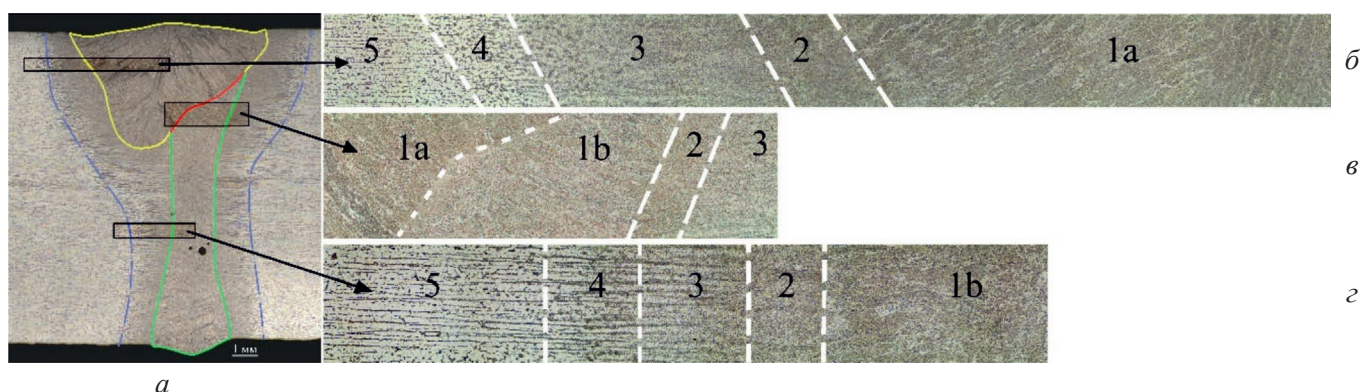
Микроструктура сварного соединения гибридной лазерно-дуговой сварки:
